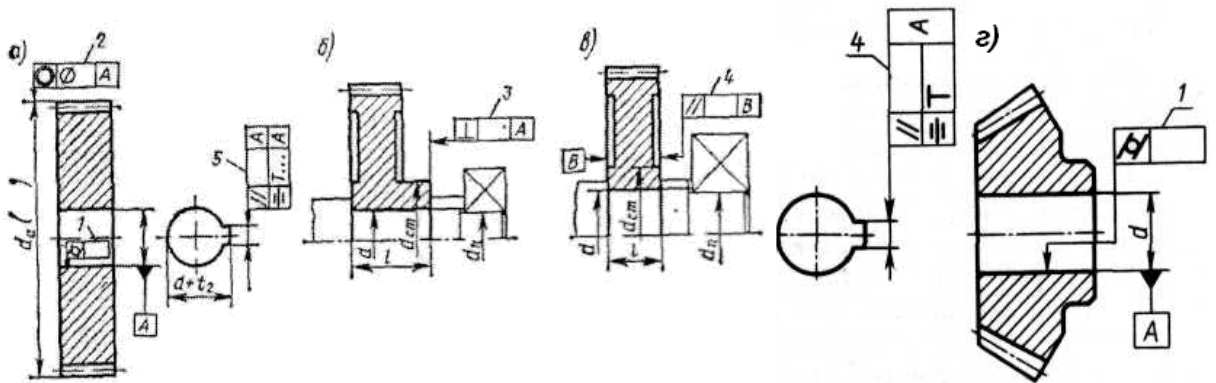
Допуски циліндричності посадочних поверхонь шестірні
